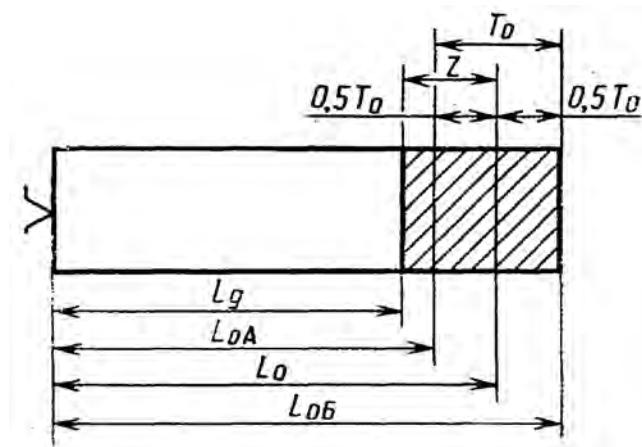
Схема расположения припусков и допусков: L_D - номинальный размер детали; L_0 - номинальный размер отливки; Z - припуск на механическую обработку; l_{oa} - наименьший размер отливки; l_{ob} - наибольший размер отливки; T_0 - допуск отливки
